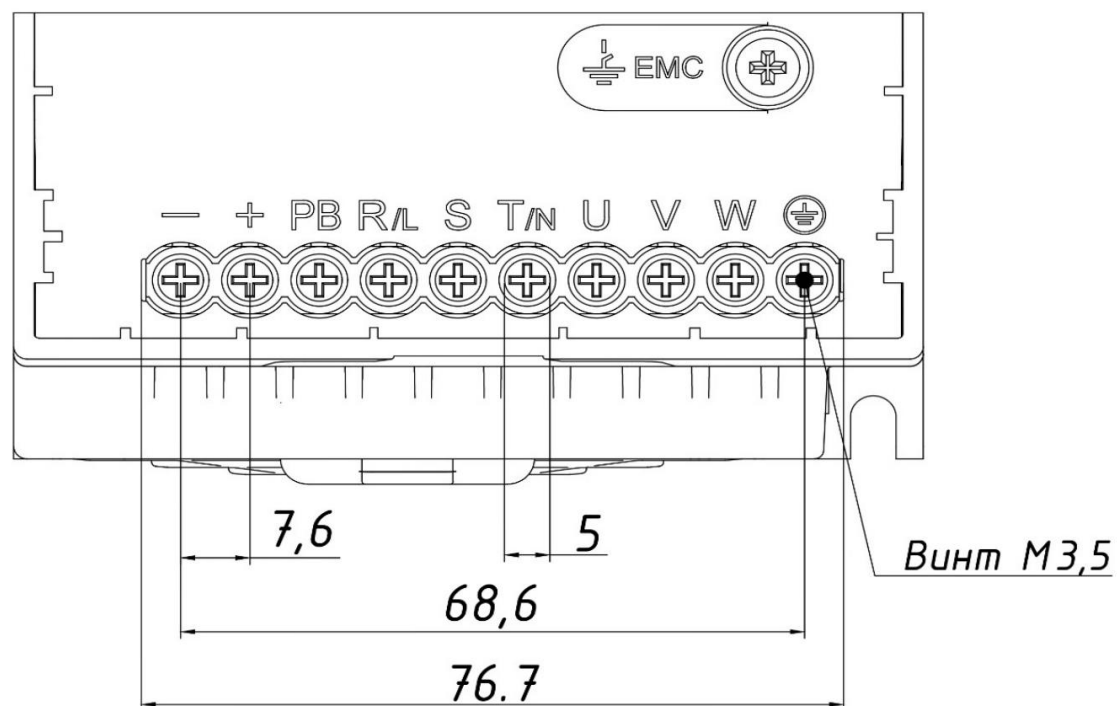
Размеры клемм цепи питания, типоразмер B2
